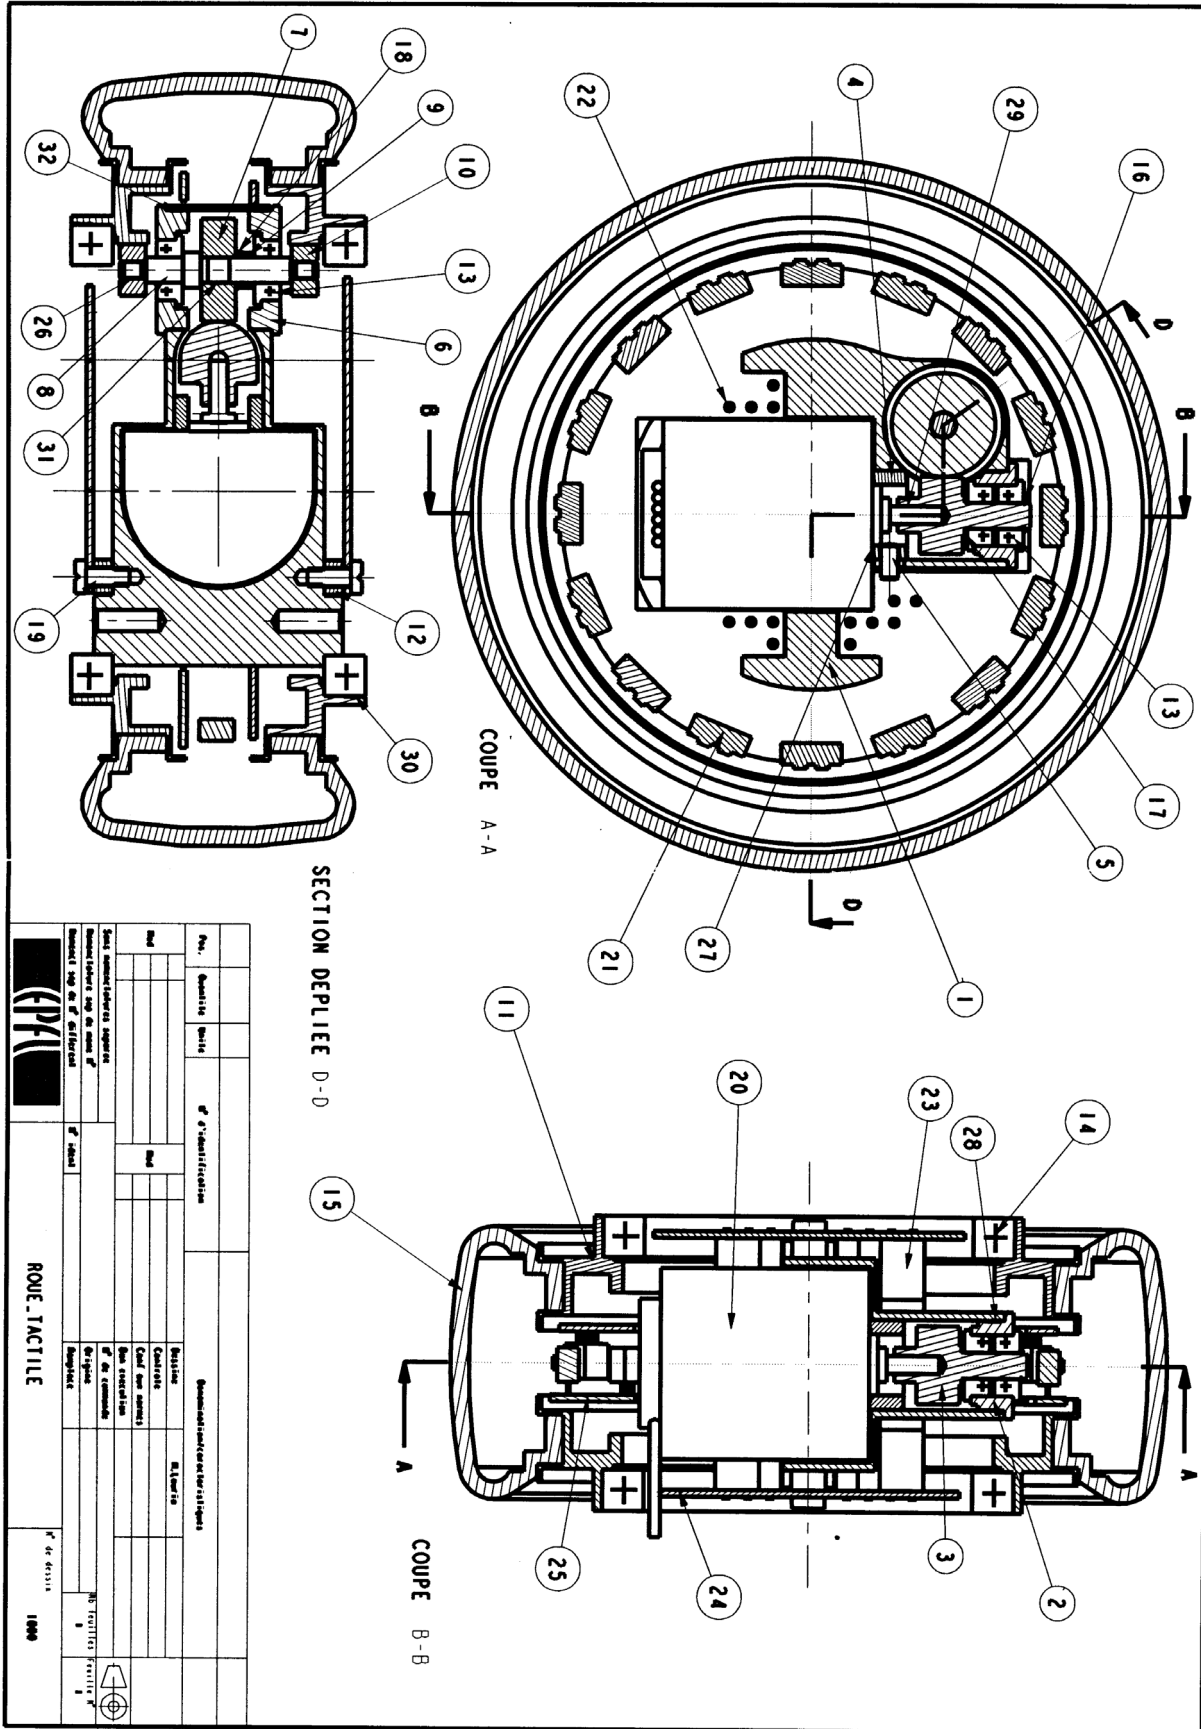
dessin d'ensemble d'une roue tactile intégré
